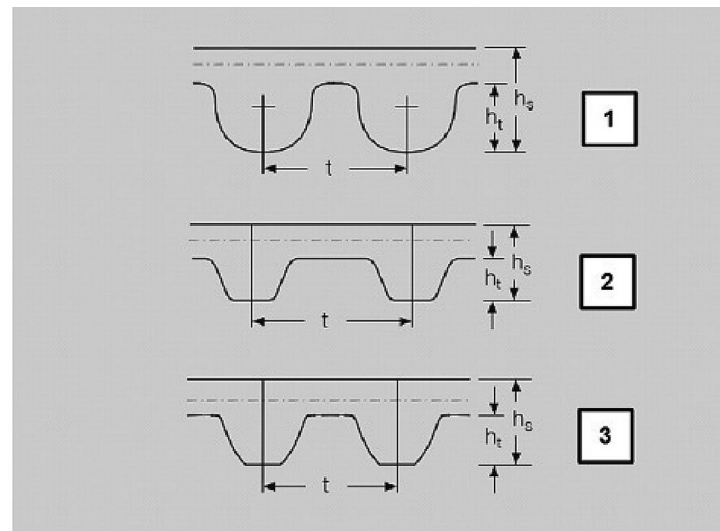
Основные профили зубьев зубчатых ремней ГРМ
